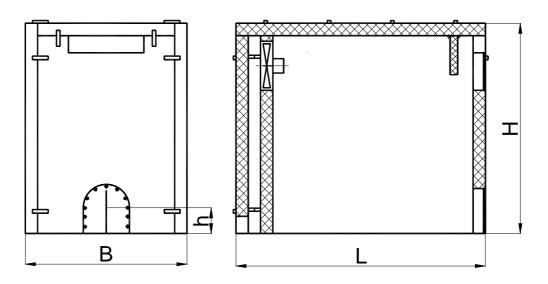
Звукоизоляционный кожух приспособленный для всасывания воздуха из окружающей среды.
